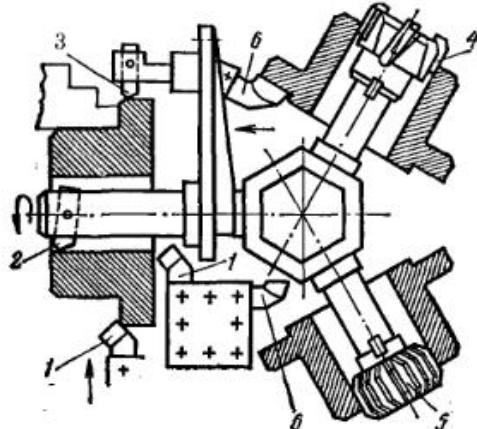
Схема операционной обработки втулки на револьверном станке с вертикальной револьверной головкой
